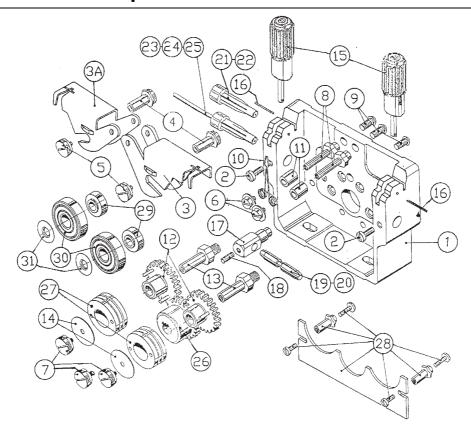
/7a Explosionszeichnung Drahtvorschubeinheit 4-Rollenantrieb / exploded view wire feed 4-rolls drive
